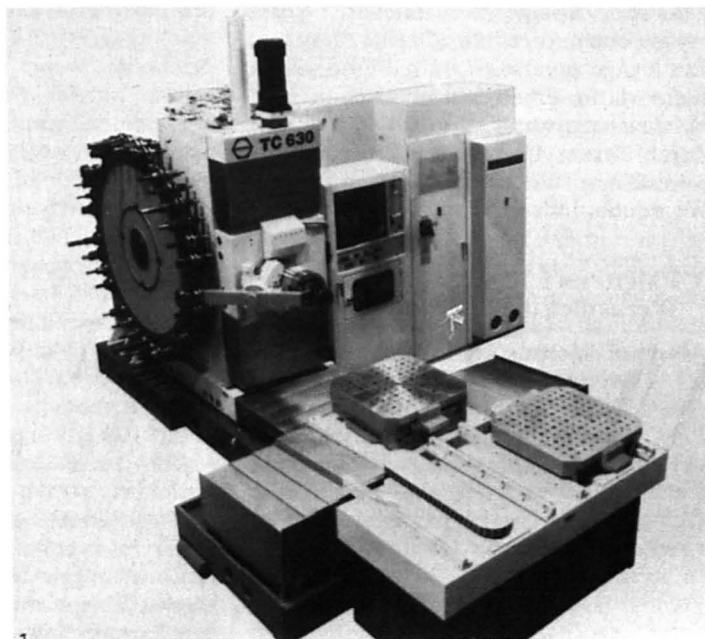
Horizontales Bearbeitungszentrum Fritz Werner TC 630 mit Palettenwechsler.
